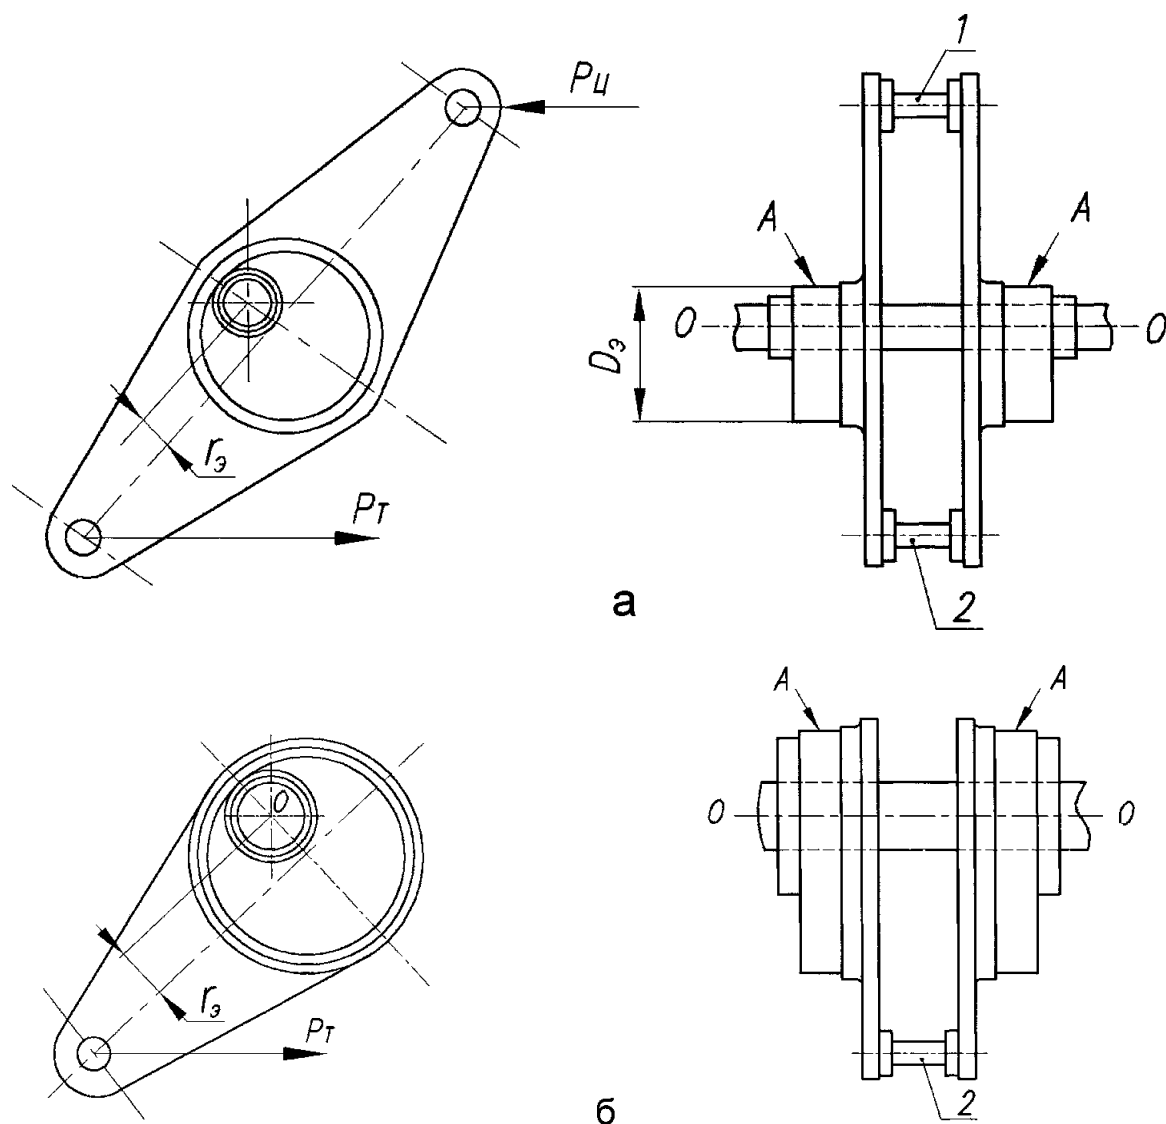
Схема установки эксцентриковых втулок с рычагами на оси ходовых колёс:
